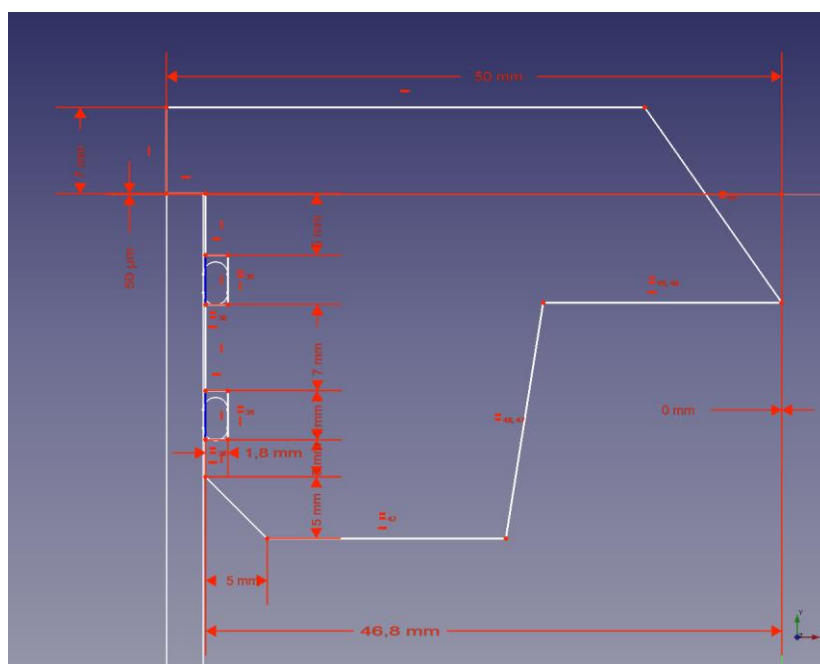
Plano de Cajera para hacer simetría circular. Fuente Propia.
